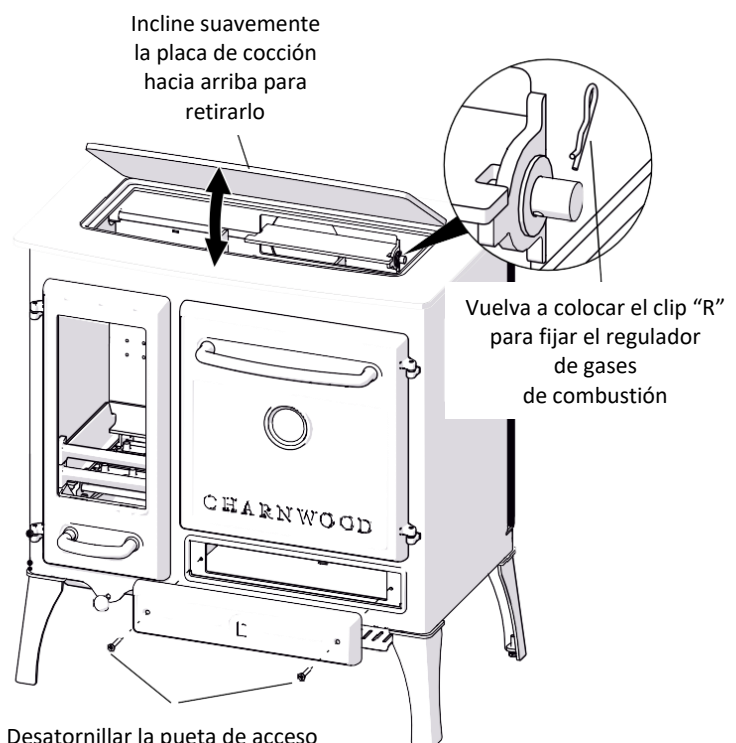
Placa de cocción, regulador de gases de combustión y desmontaje de la puerta de acceso.
